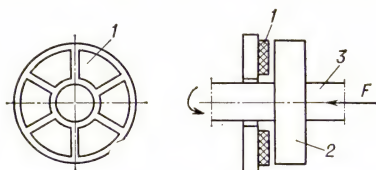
Схема осевого подшипника скольжения: 1 — подпятник; 2 — упорный диск; 3 — вал; F — осевая сила.
